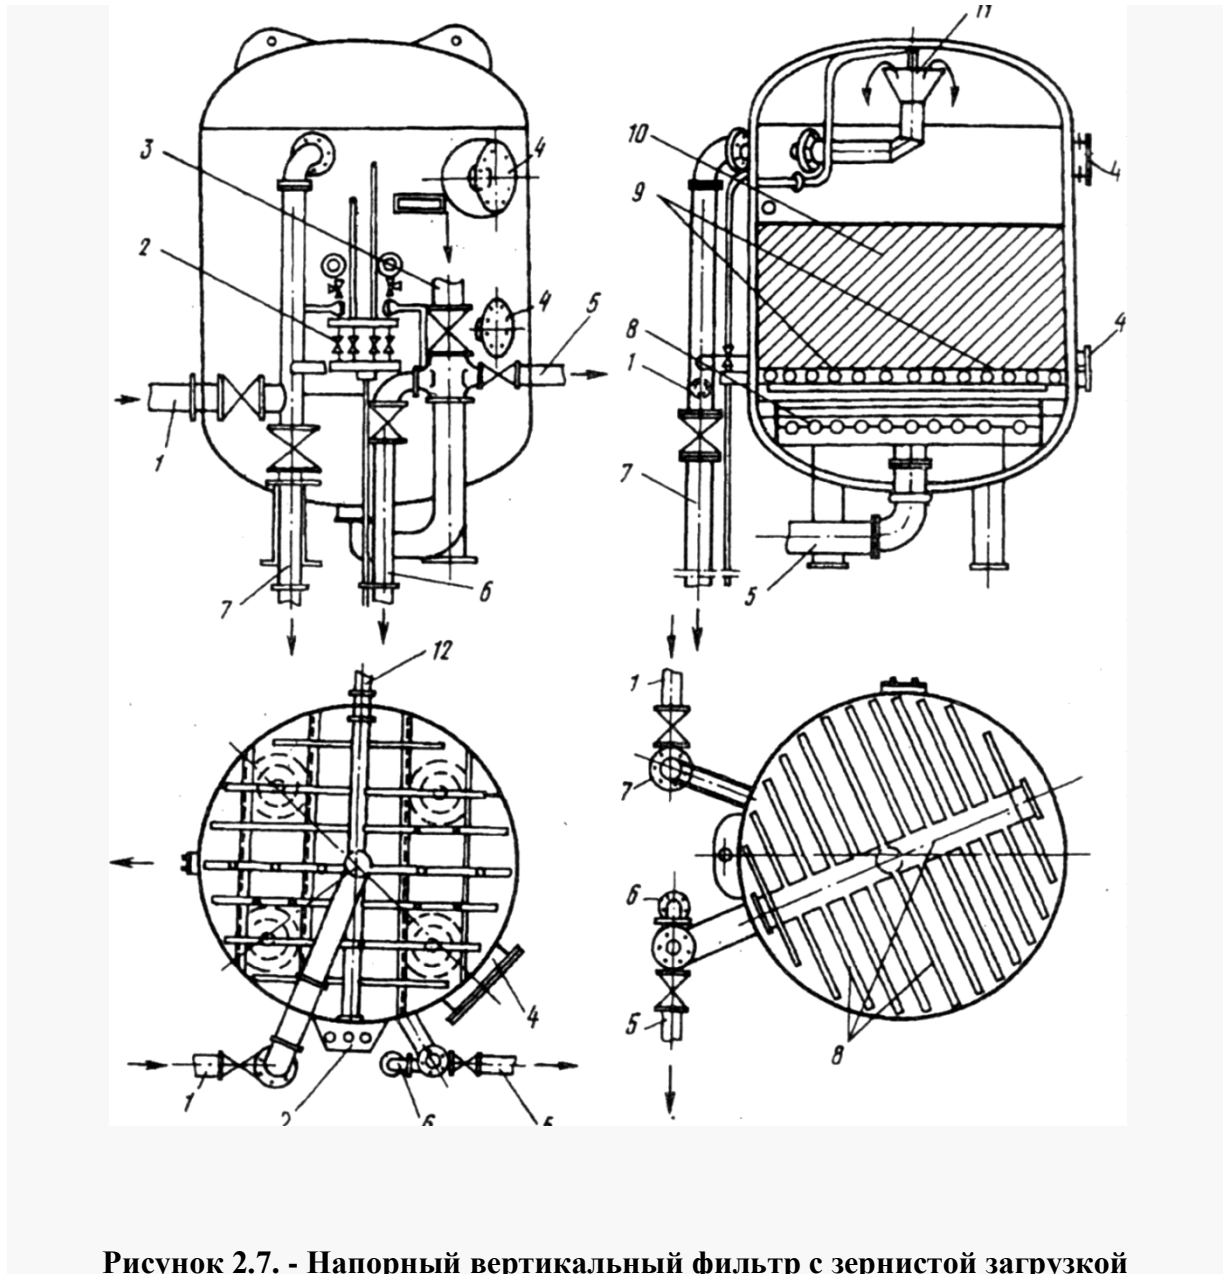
Напорный вертикальный фильтр с зернистой загрузкой
